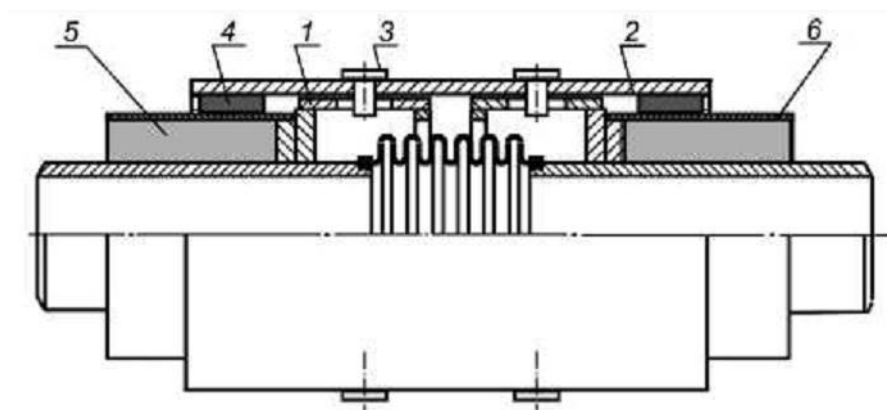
Осевое сильфонное компенсационное устройство для бесканальной прокладки
